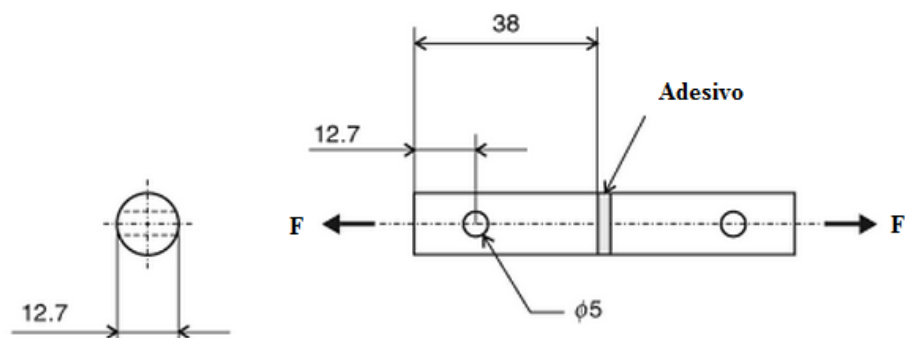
Geometria da junta de topo a topo (dimensões em mm) [2]
